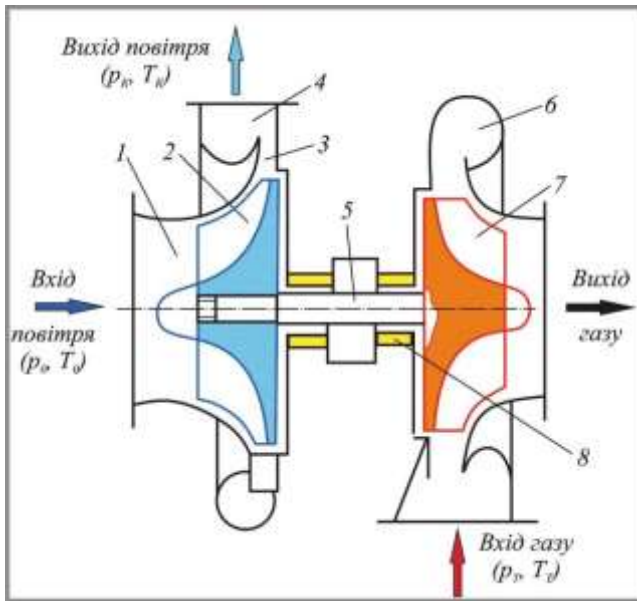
Схема відцентрового турбокомпресора: 1 – приймальний патрубок компресора; 2 – колесо компресора; 3 – дифузор компресора; 4 – нагнітальний патрубок компресора; 5 – вал ТКР; 6 – сопловий апарат турбіни; 7 – колесо турбіни; 8 – підшипник ковзання
